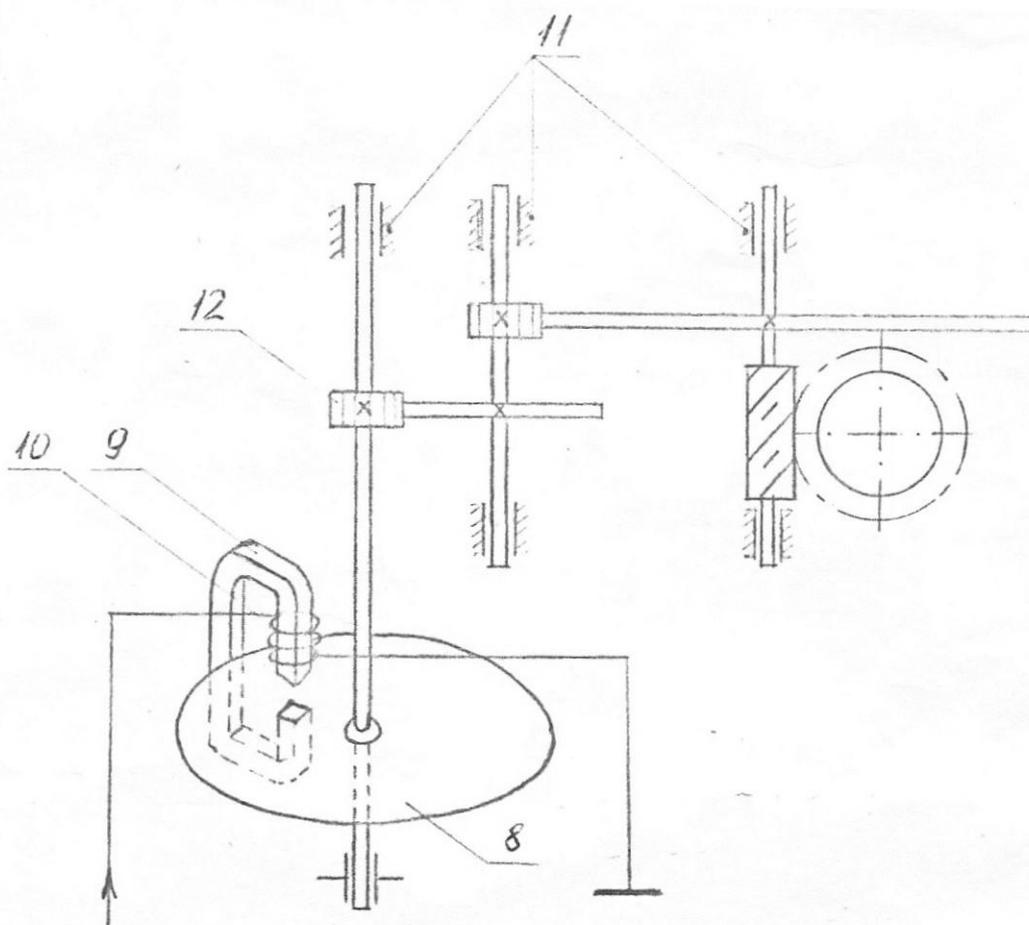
Исполнительный механизм (счетчик) устройства для замера загрузки и наработки двигателя
